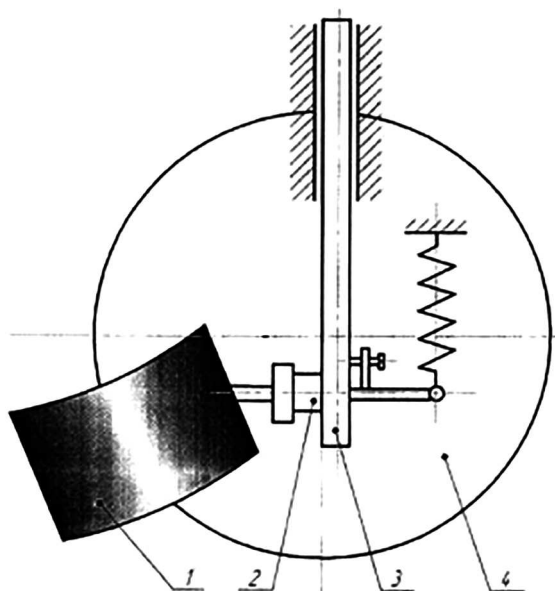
Схема приспособления: 1 – подпружиненный щиток; 2 – регулировочный механизм; 3 – стойка; 4 – диск
